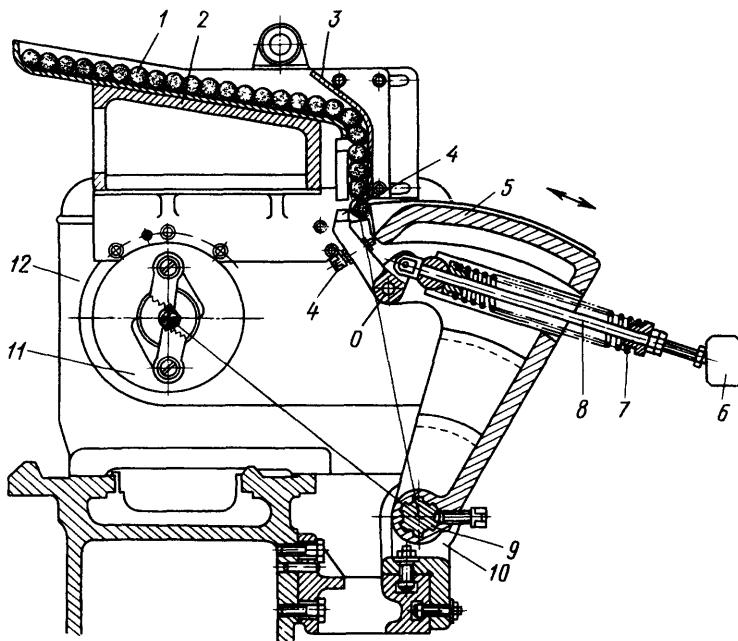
Магазинное загрузочное устройство для токарного станка
